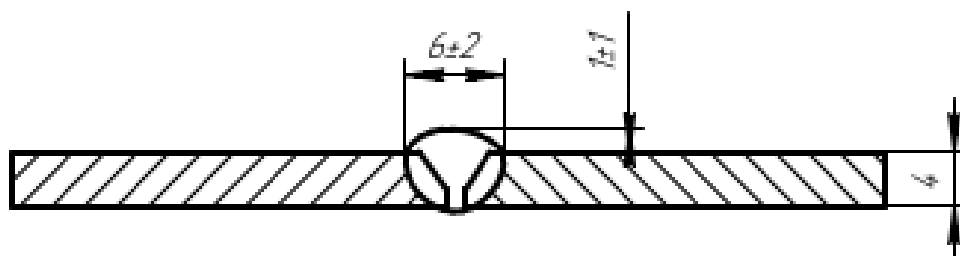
Геометрические параметры сварки пластин
